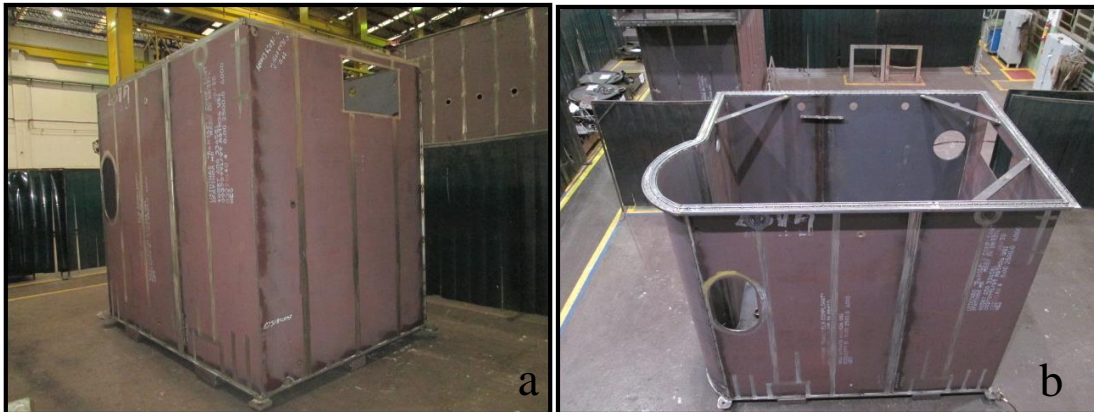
Montagem Tanque e 5b Montagem flange sobre o tanque
